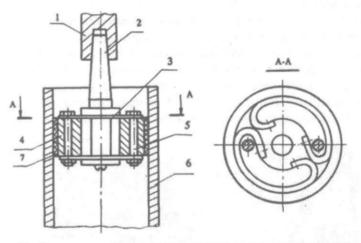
Схема устройства для латунирования гильз цилиндров: 1- механизм вращения; 2- приводной вал; 3- диск; 4- натирающий инструмент; 5- ось; 6- поверхность обрабатываемой детали; 7- чехол
